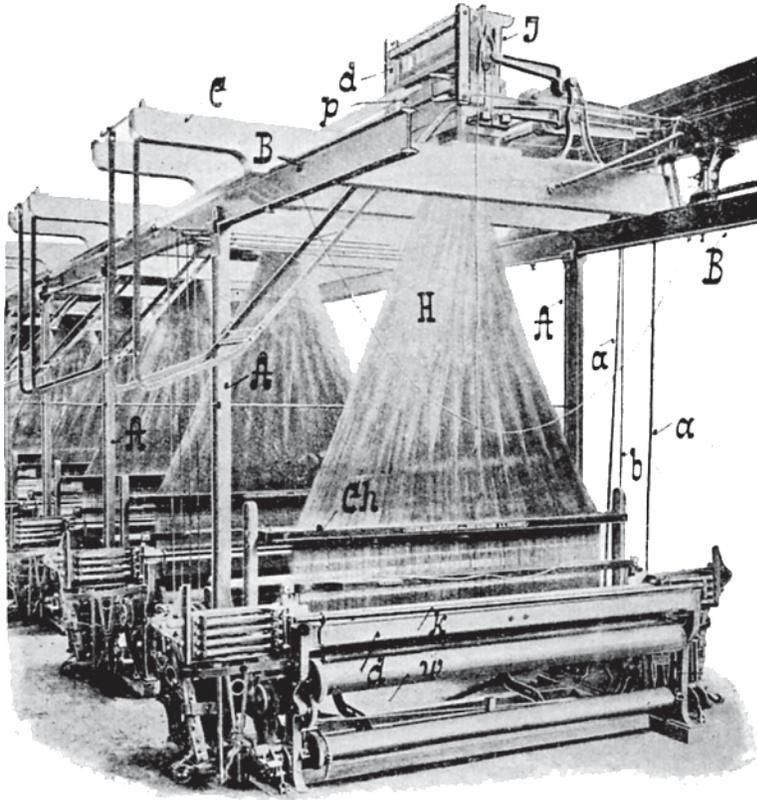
Buckskinstuhl mit Jacquardmaschine und Harnischeinrichtung.
